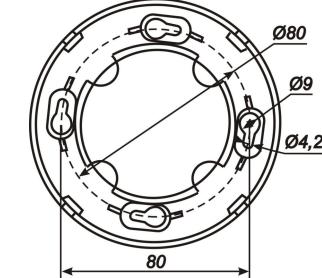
Расположение отверстий для крепления базы извещателя
